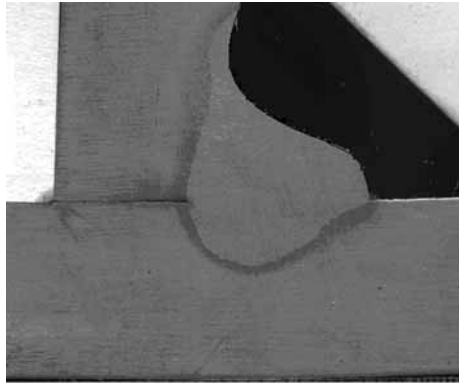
Формирование углового шва при сварке под флюсом листов из стали 09Г2С толщиной 20 мм при токе 900 А и скорости сварки 5 мм/с
